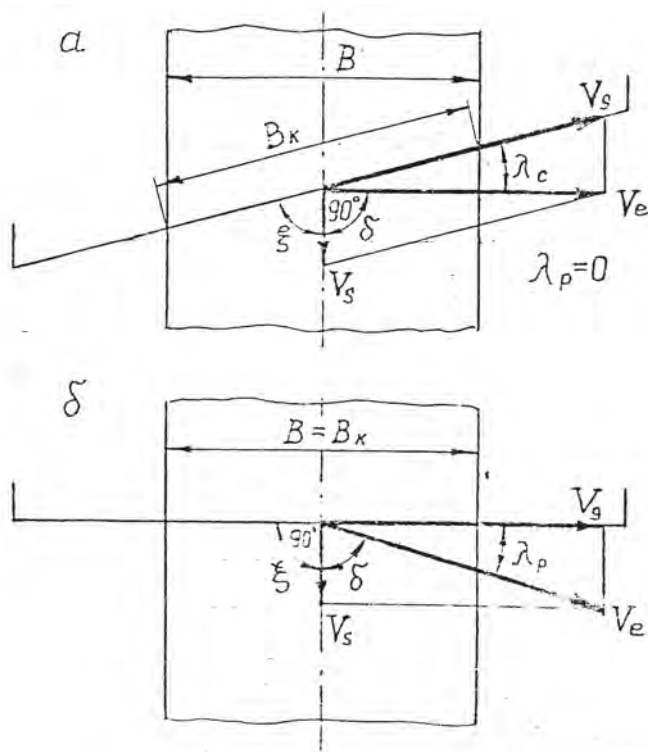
Схема резания с касательным движением лезвия режущего диска.
